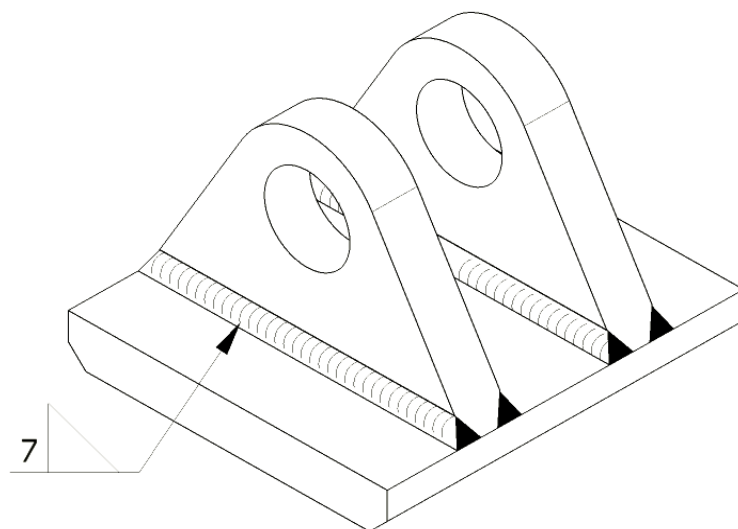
Unión soldada en un apoyo del cilindro hidráulico
